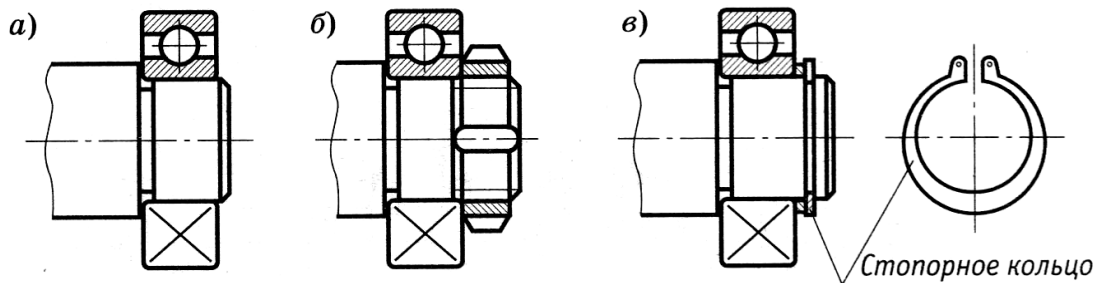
Цапфы валов и осей под подшипники качения: *а* – цилиндрическая с заплечиком; *б* – с креплением гайкой; *в* – с креплением стопорным кольцом
